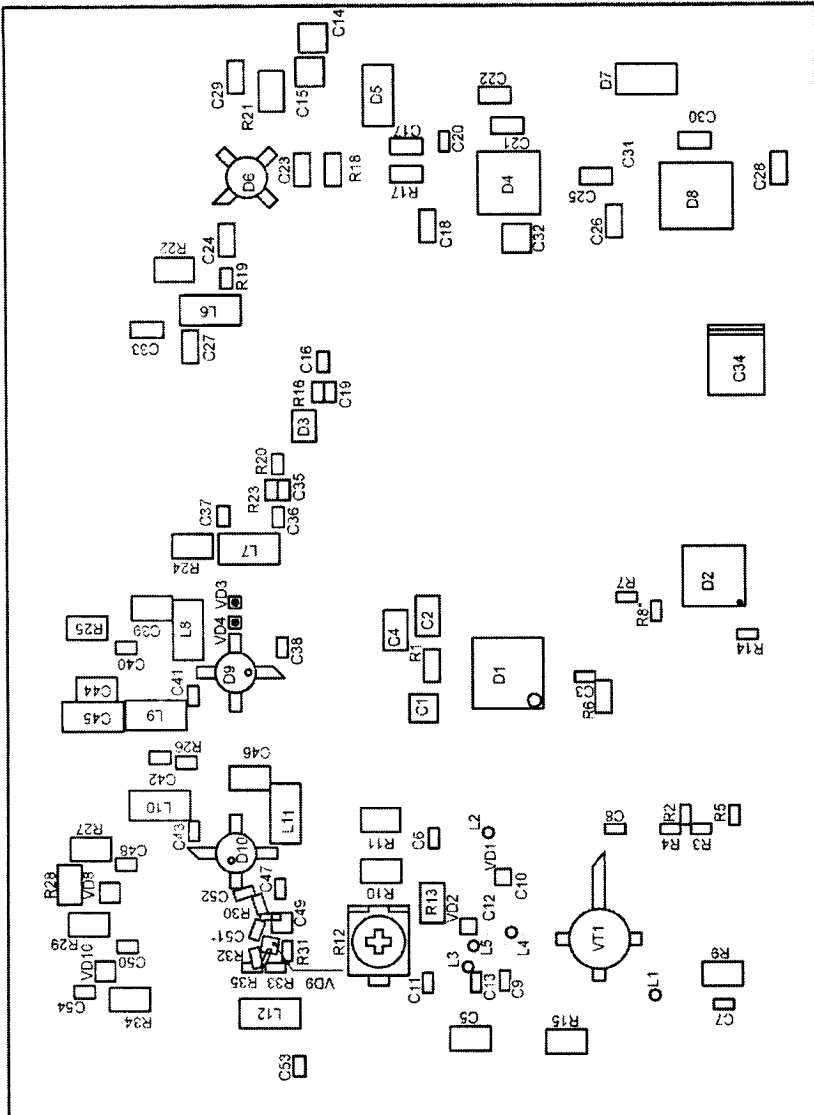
План размещения элементов на плате ГУН 0,01- 2,5 ГГц
